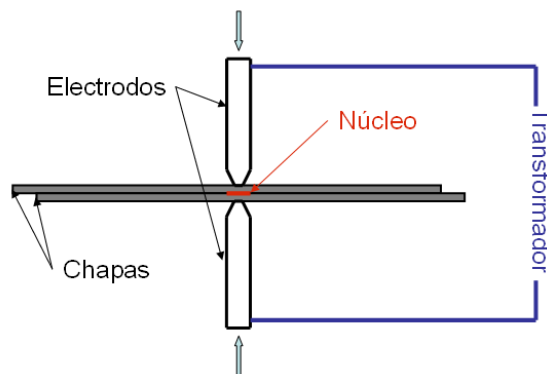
Soldadura por resistencia eléctrica [16].
